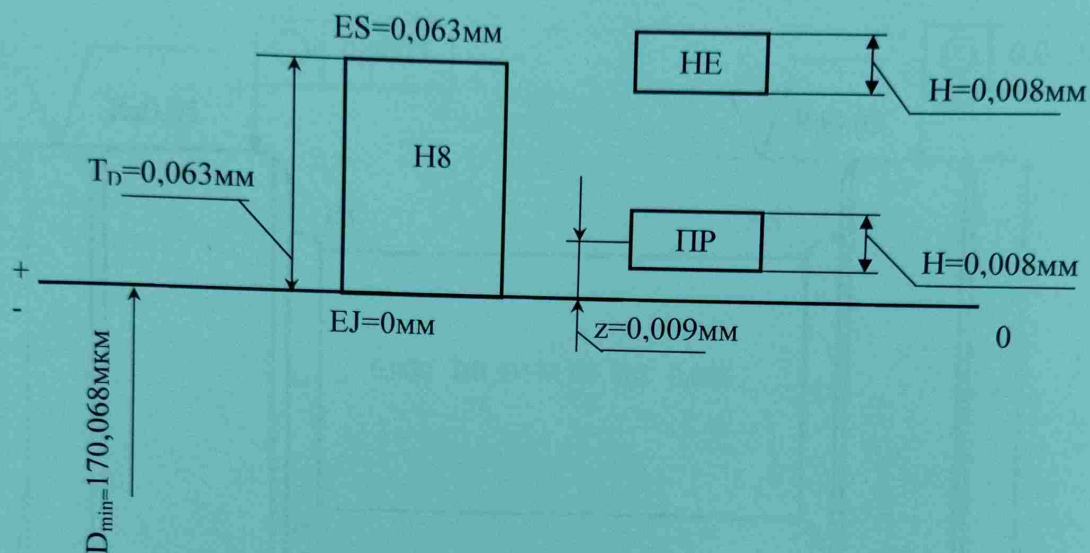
Схема расположения полей допусков для калибра-пробки.
